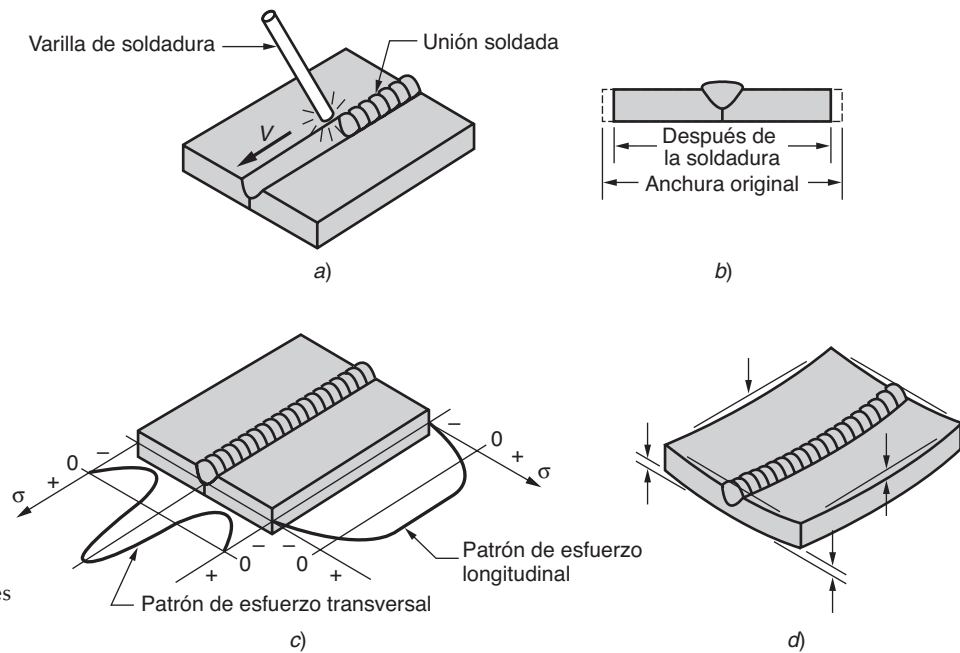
a) Soldadura empalmada de dos placas; b) encogimiento a través de la anchura del ensamble soldado; c) patrón de esfuerzos residuales transversales y longitudinales y d) combadura probable en el ensamble soldado.
